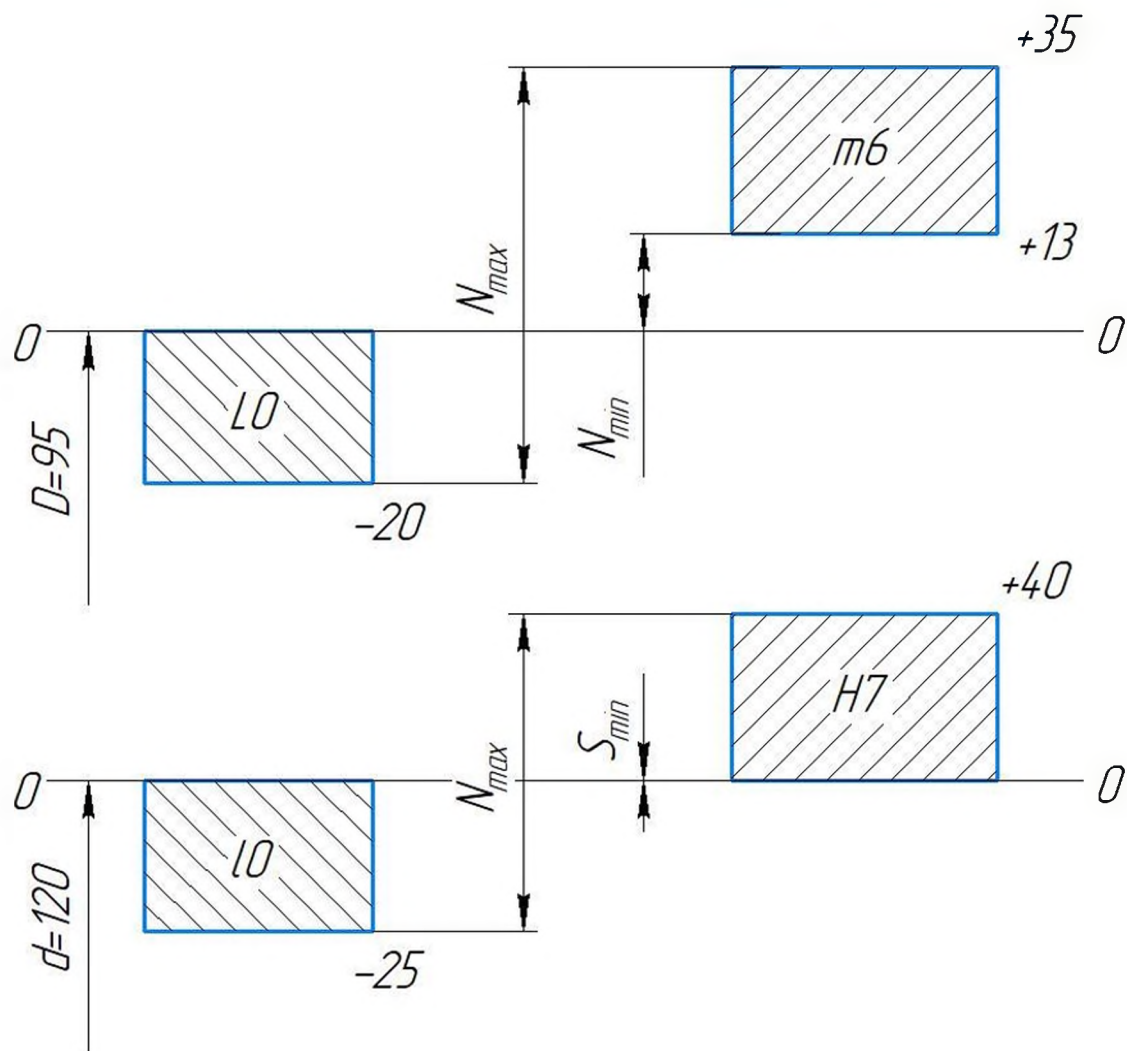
Схема полів допуску підшипника кочення
